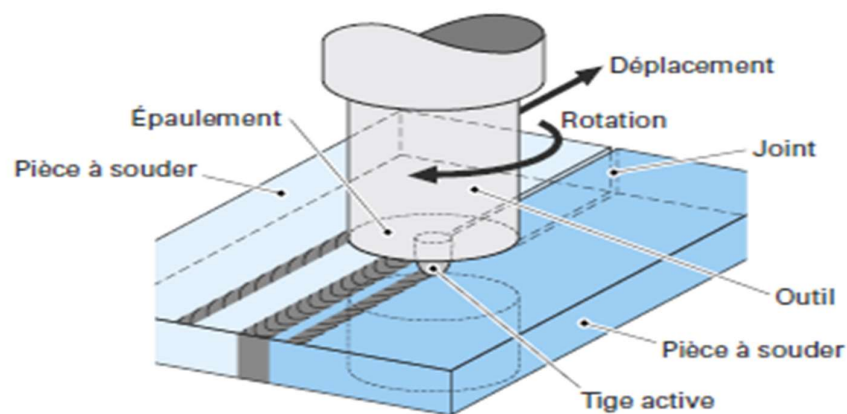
Principe de soudage par friction malaxage [29]
